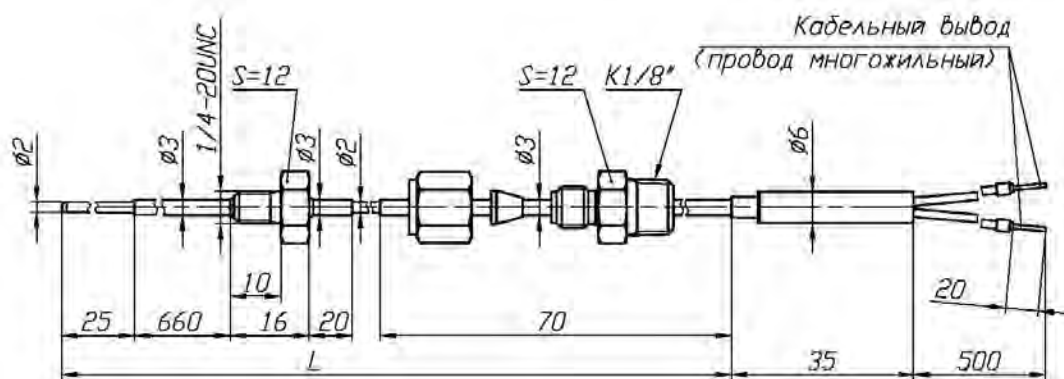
е – Габаритный чертеж ТТ модели ТХА 001.06Сп с двумя установочными узлами
